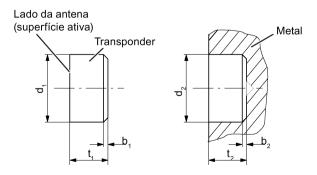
Montagem do MDS D421 encastrado em metal para ferramentas
